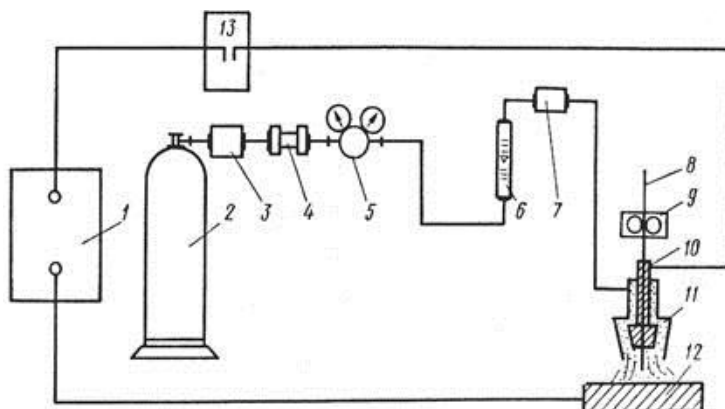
Схема подачи углекислого газа: 1 – источник сварочного тока; 2 – баллон с углекислотой; 3 – подогреватель; 4 – влагопоглотитель; 5 – редуктор; 6 – расходомер; 7 – отсекающий газ; 8 – наплавочная проволока; 9 – подающий механизм; 10 – мундштук; 11 – сопло горелки; 12 – деталь; 13 – контакты выключателя сети
